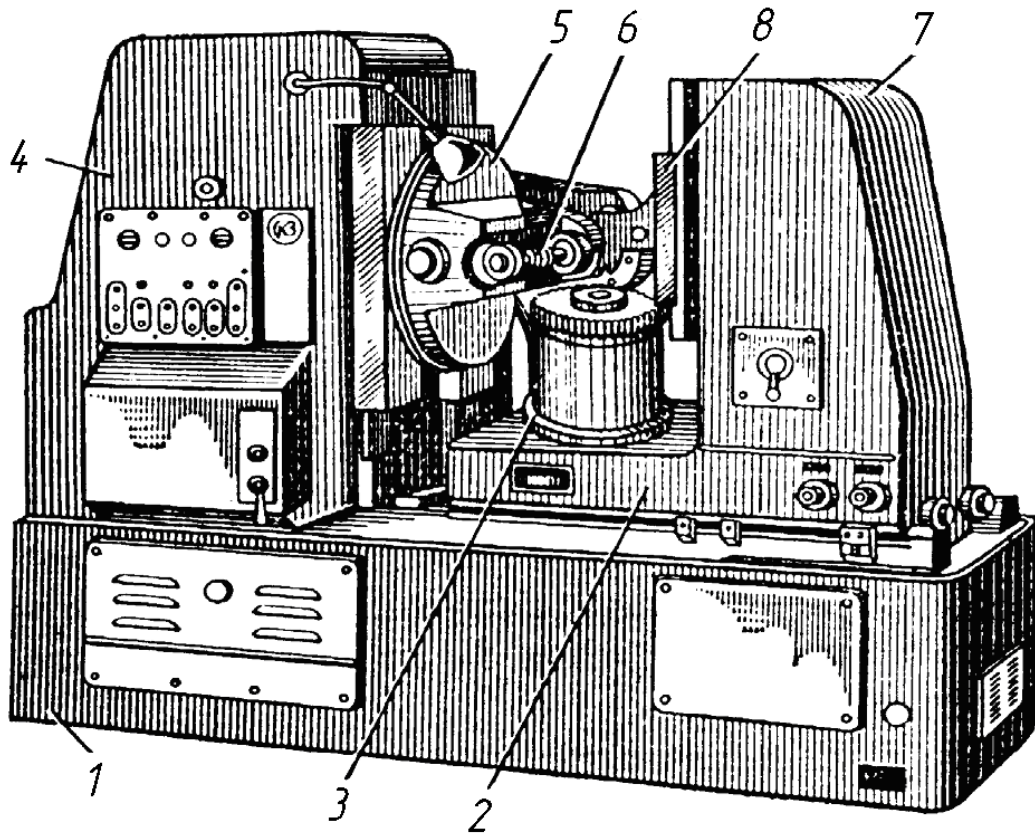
Зубофрезерный полуавтомат мод. 5К301
